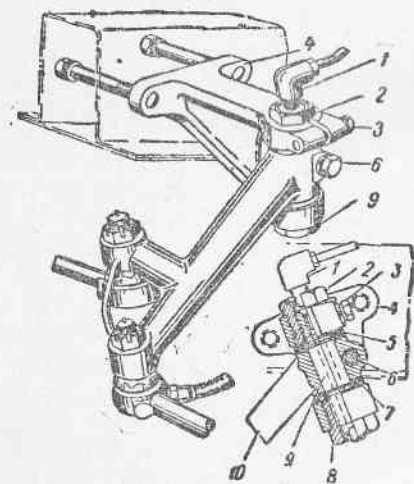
Маятниковый рычаг рулевого привода автомобиля М-21 «Волга»
